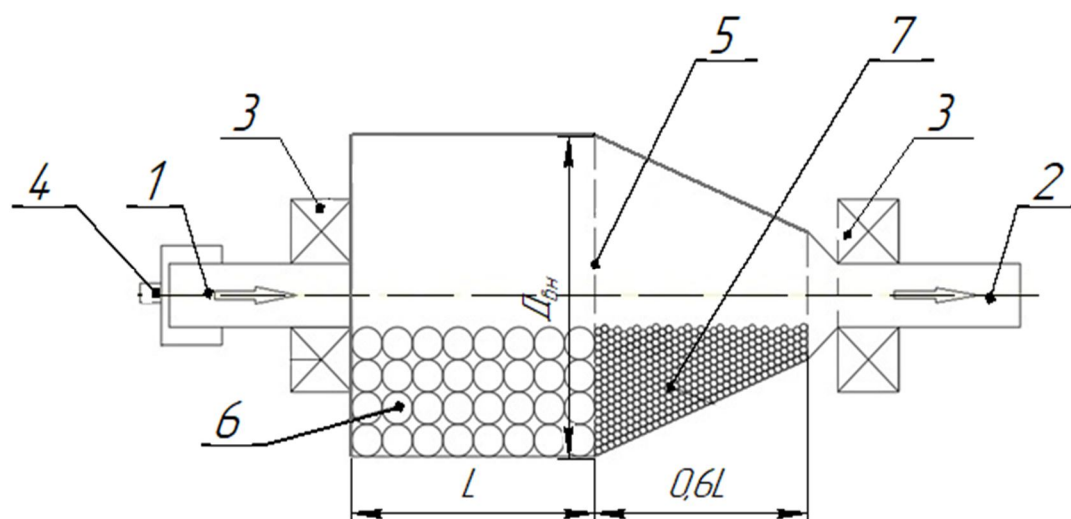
Схема шаровой мельницы: 1 – впускающий патрубок; 2 – выпускающий патрубок; 3 – подшипники качения; 4 – жиклер; 5 – решетка перфорированная; 6 – крупные шары; 7 – мелкие шары
